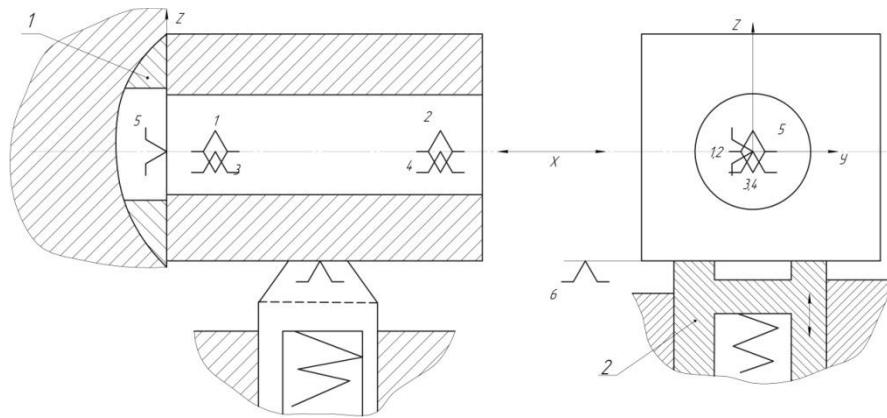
Схема базирования корпусной детали с использованием разжимной оправки, самоустанавливающейся (поз. 1) и подпружиненной (поз. 2) опор приспособления
